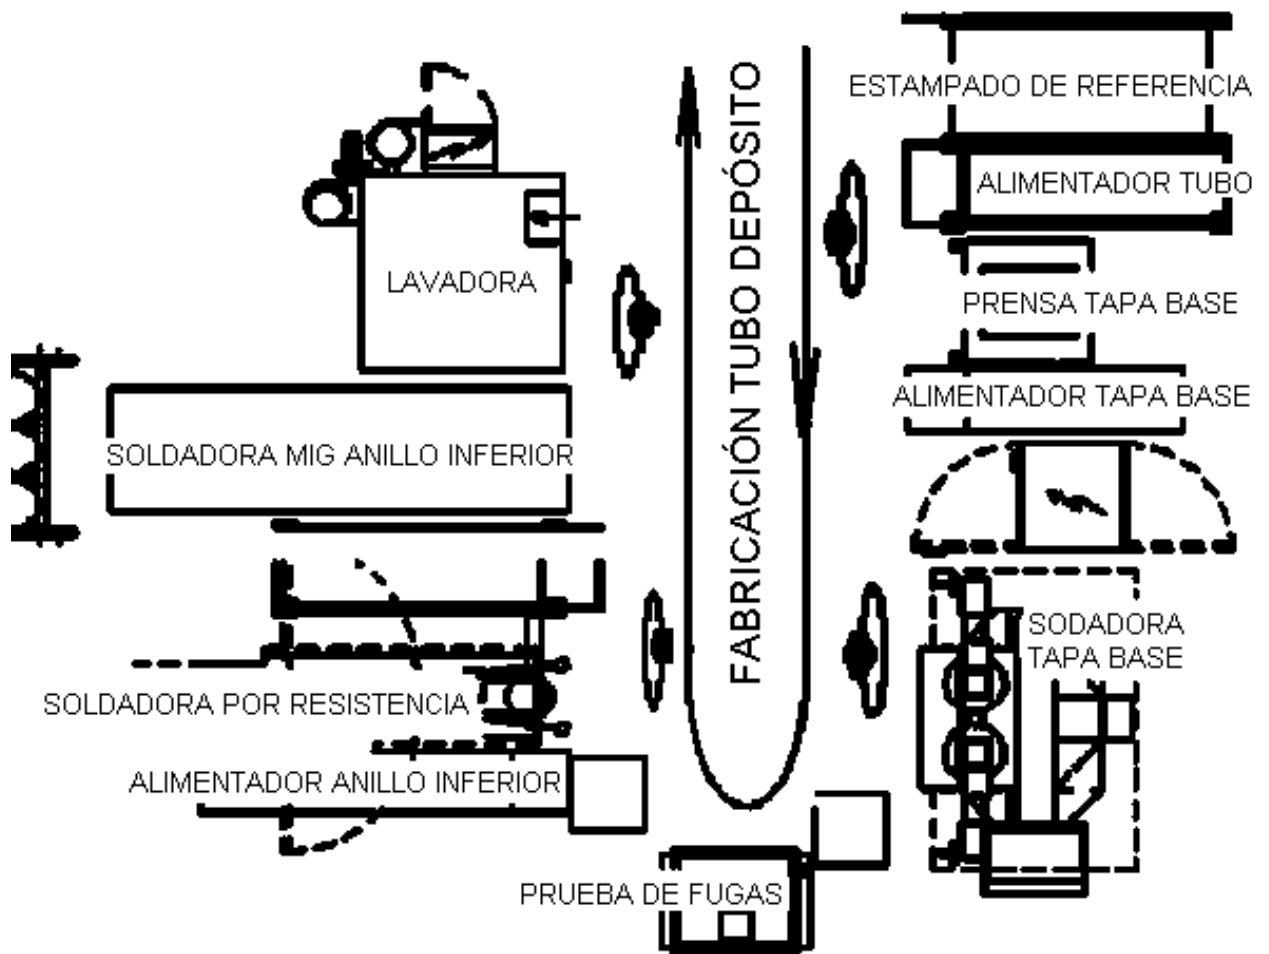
Línea de fabricación del conjunto tubo depósito
